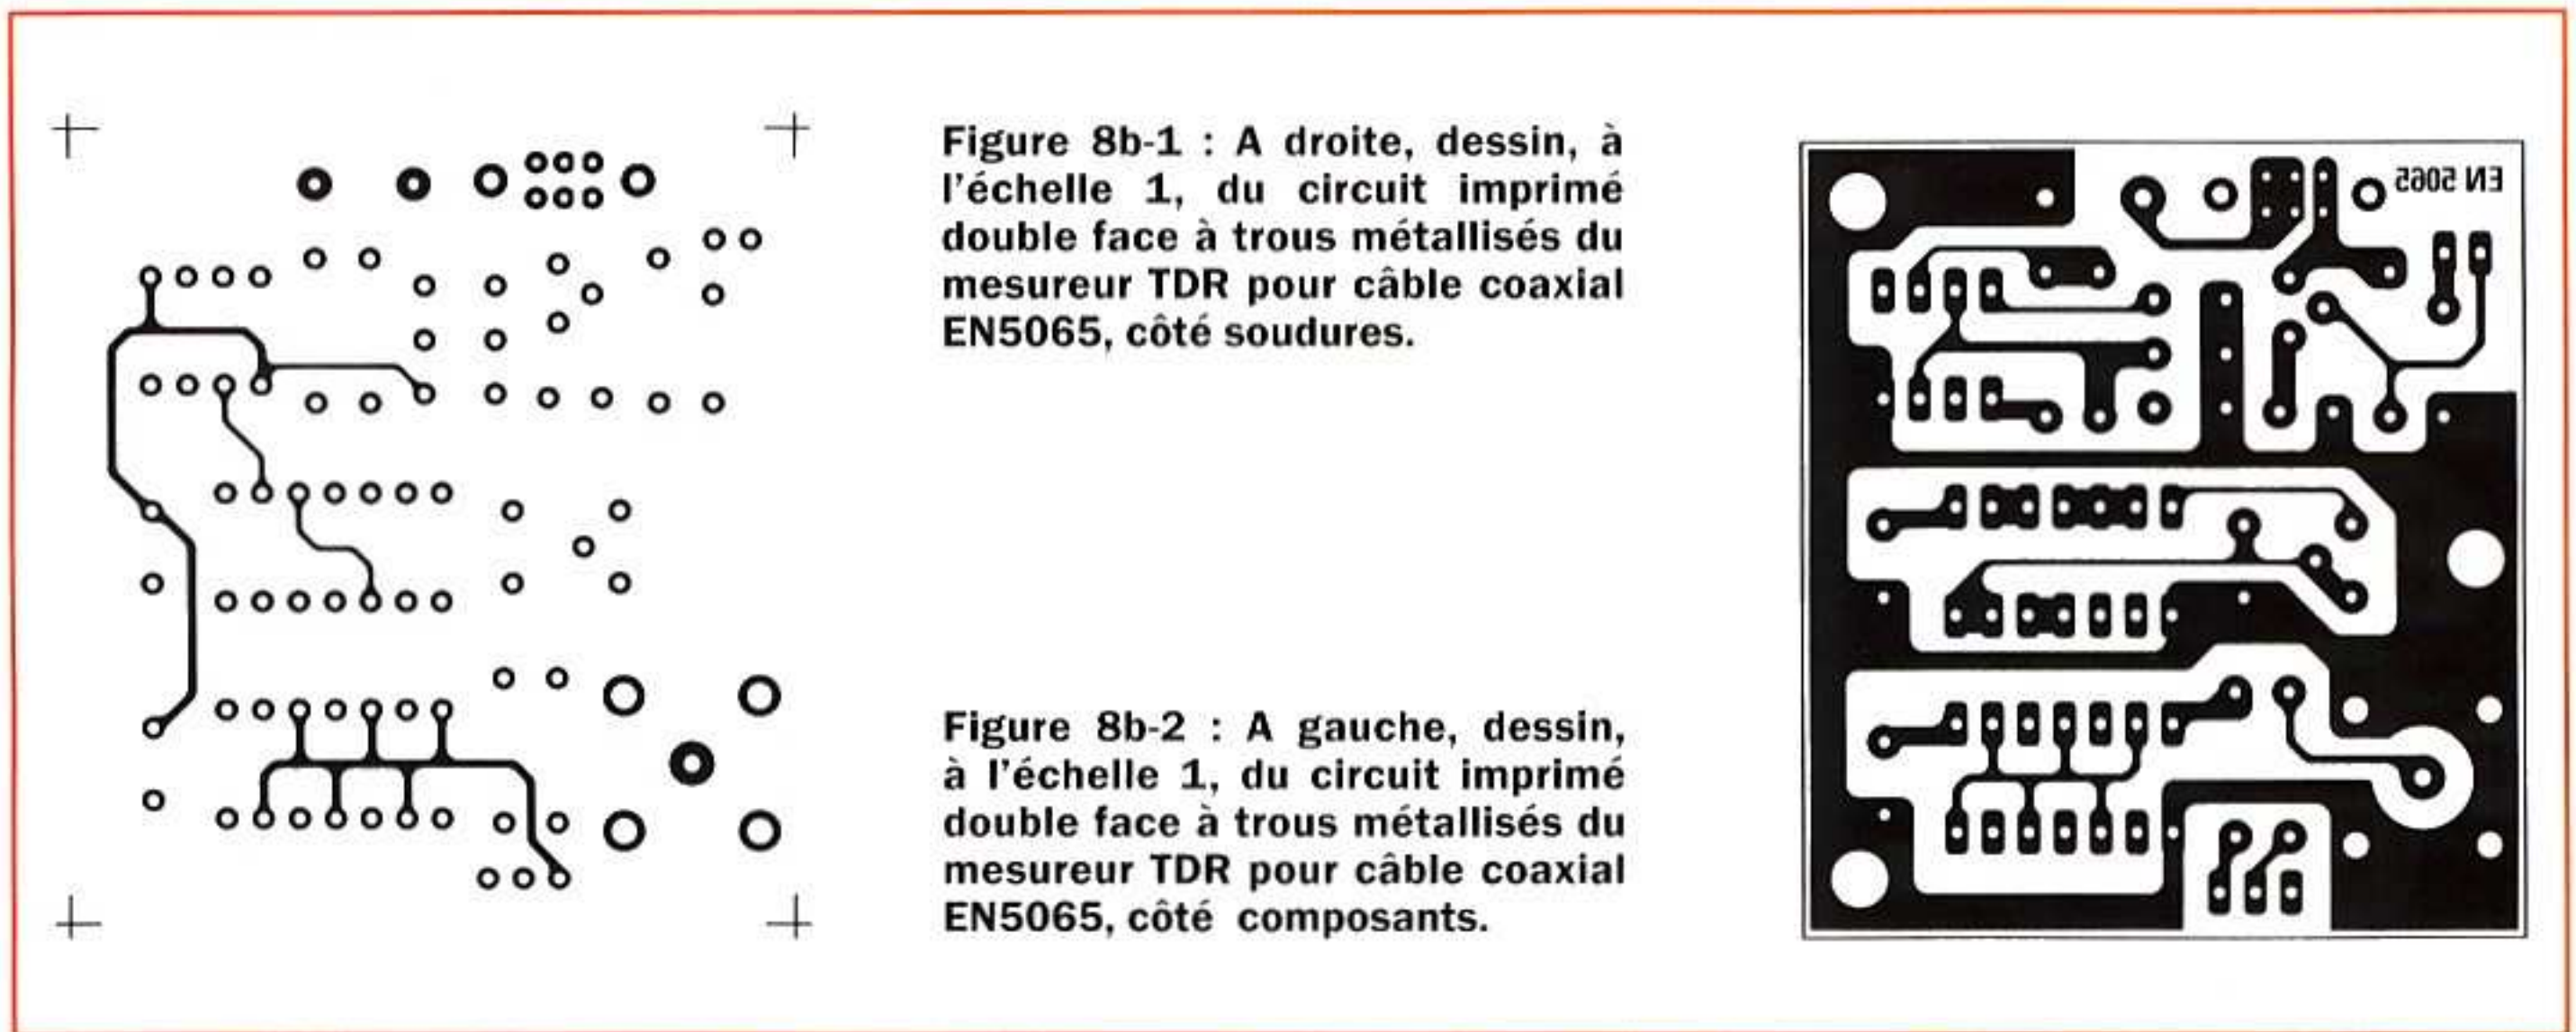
1 : A droite, dessin, à l'échelle 1, du circuit imprimé double face à trous métallisés du mesureur TDR pour câble coaxial EN5065, côté soudures.
